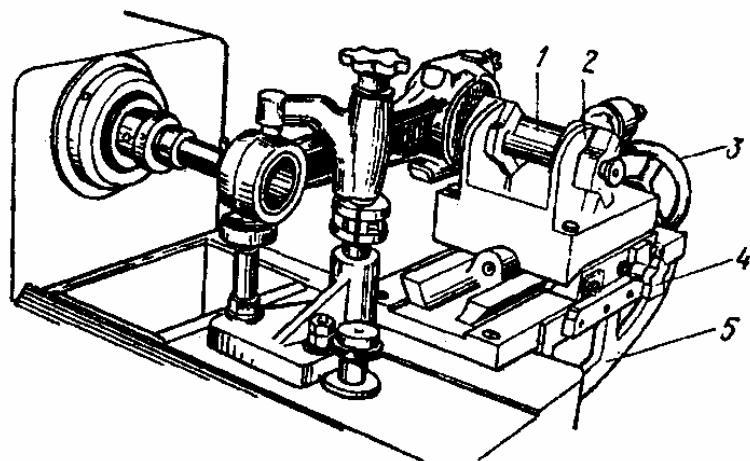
Встановлення шатуна на верстаті УРБ-ВП для розточування верхньої головки та її втулки: 1 – оправка; 2 – призма каретка; 3 – маховик пересувної каретки; 4 – стопорний гвинт; 5 – кронштейн
